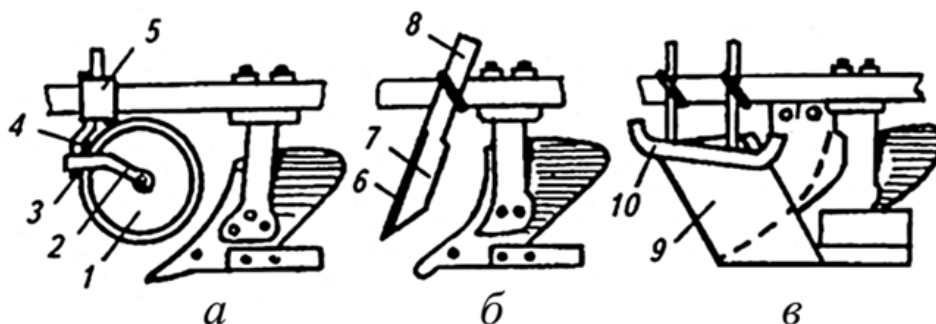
Типи ножів. 1 – диск; 2 – вилка; 3 – корончата шайба; 4 – колінчата вісь; 5 – шарнір; 6 – лезо; 7 – черенковий ніж; 8 – стояк; 9 – полозковий ніж; 10 – опорна лижа.
